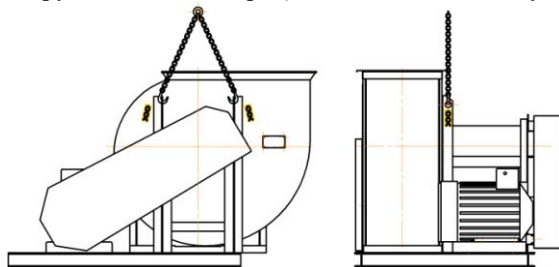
Схема строповки центробежных вентиляторов 5-й конструктивной схемы.
